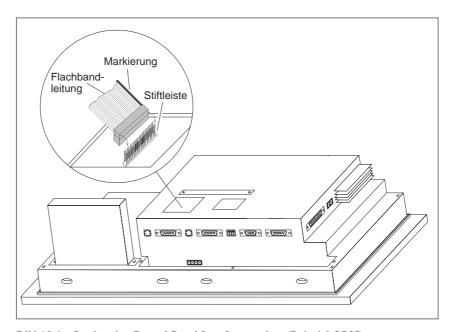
Stecker des Control Panel Interface stecken (Beispiel OP37)
